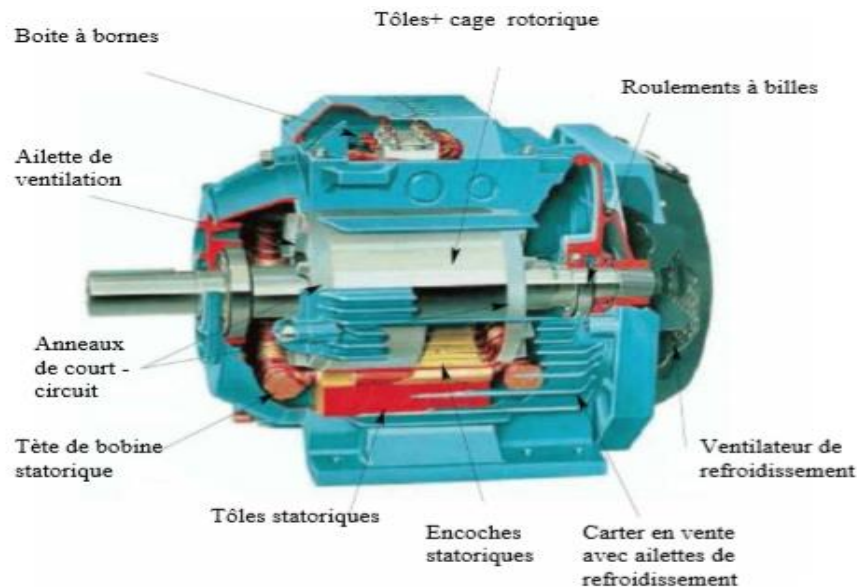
élément de constitution d'une machine a cage d'écureuil [2]
